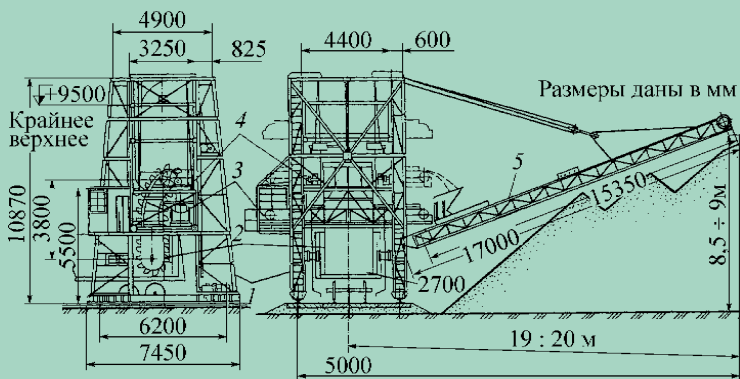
Ковшово-элеваторный разгрузчик ТР-2:
